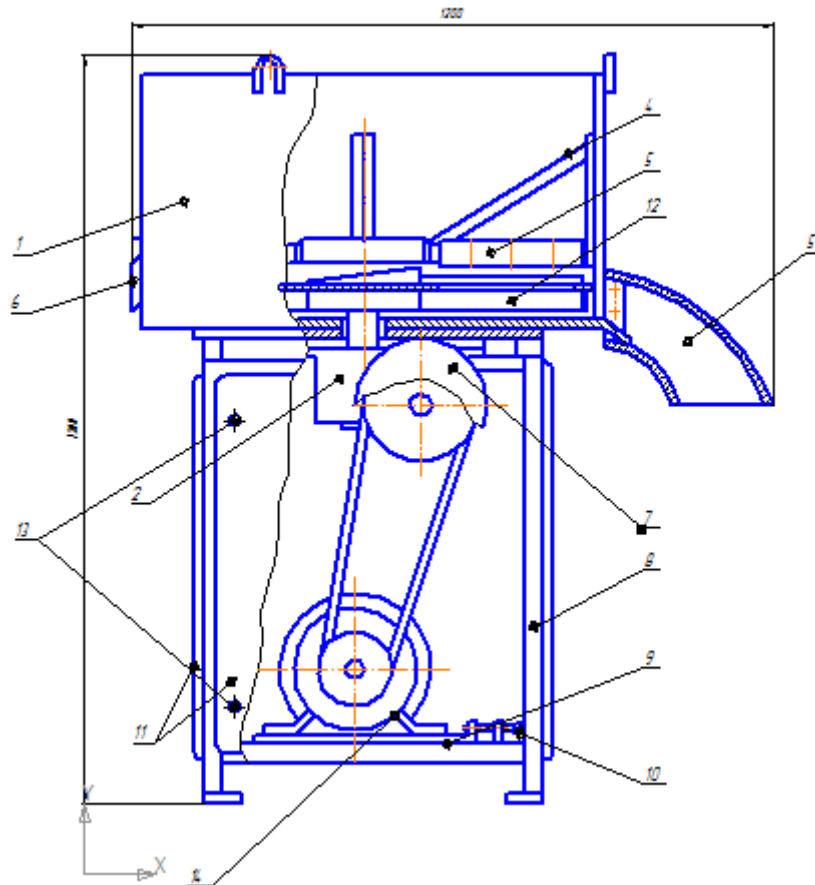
Загальний вид подрібнювача соковитих кормів
